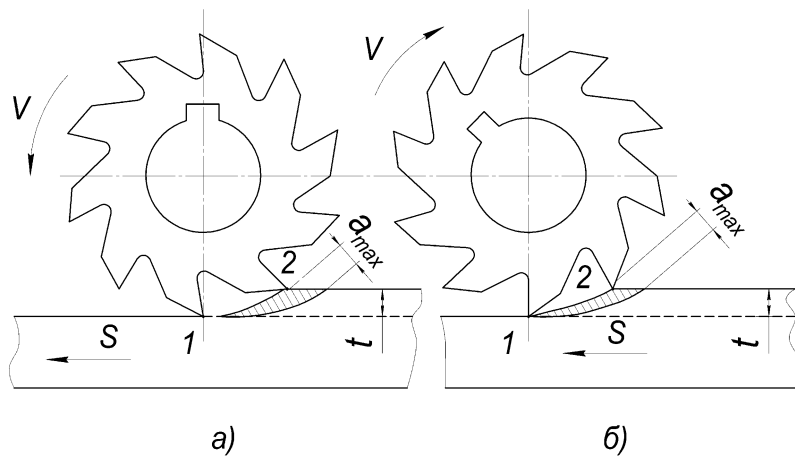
Схеми зустрічного (а) і попутного (б) фрезерування
